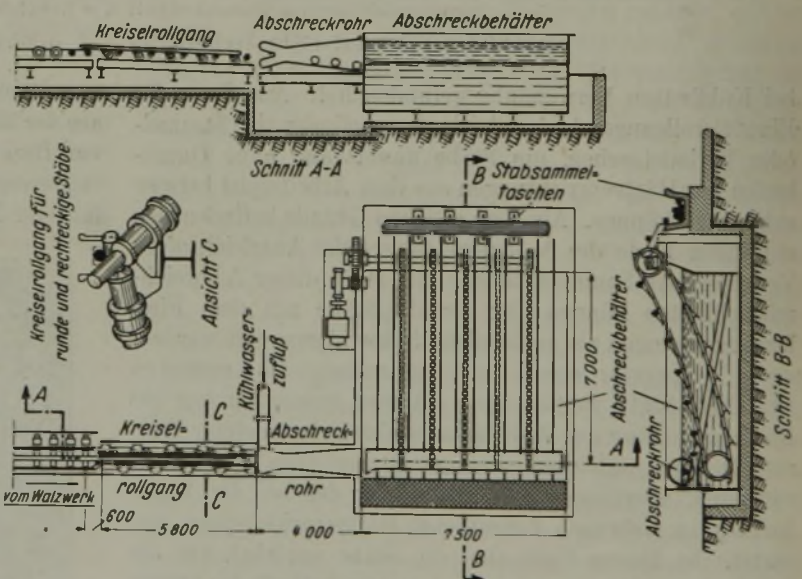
Walz-Härteanlage für Rund- und Profilstäbe.
